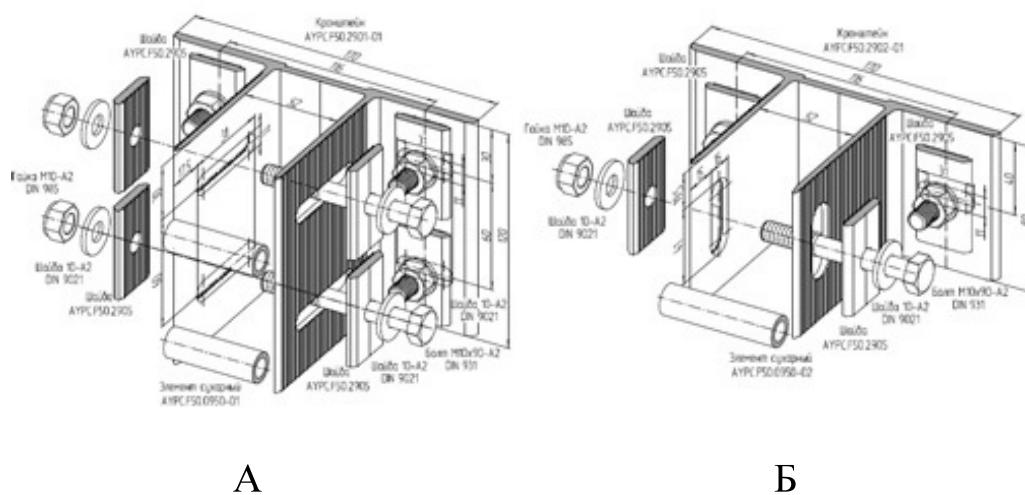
А. Комплект кріплення для фасаду навісного типу анкерний (несучий); Б. Комплект кріплення для фасаду навісного типу вітровий (рухомий)
